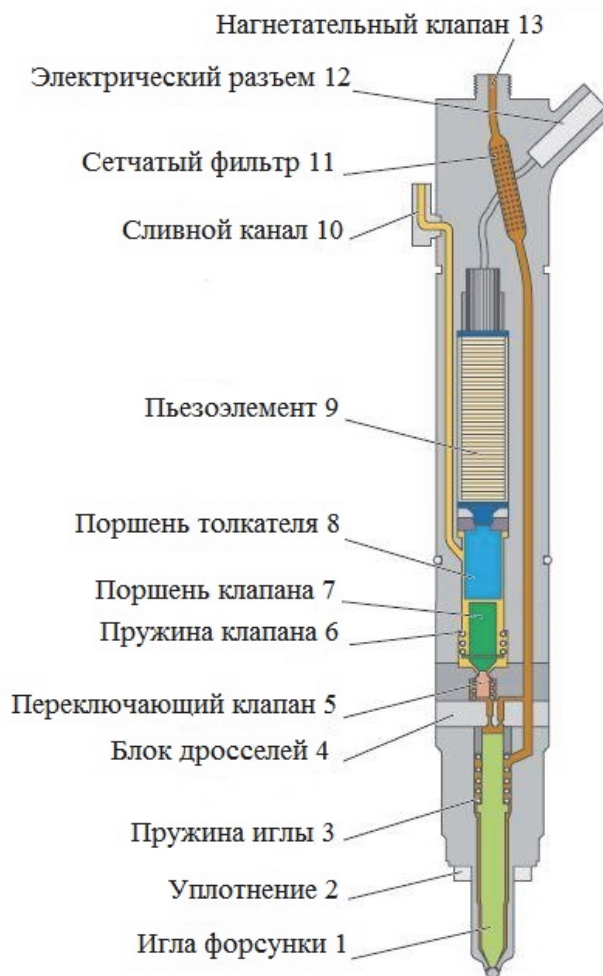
Устройство пьезоэлектрической форсунки [5]
